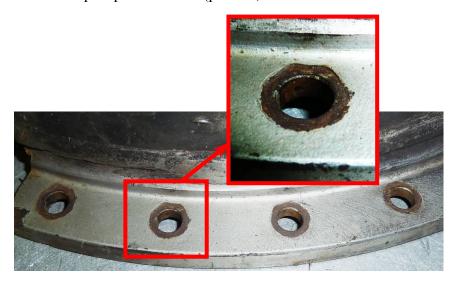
Вдавливания головок болтов в верхней части заднего фланца корпуса компрессора.
